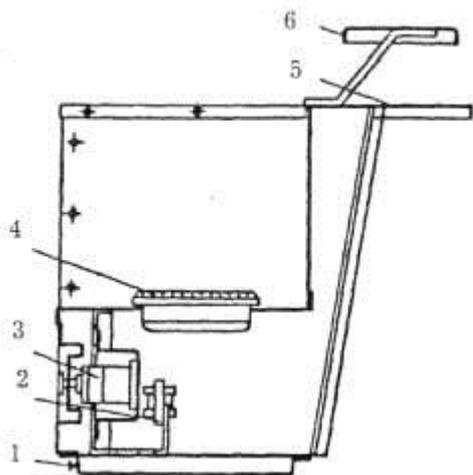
Мармит для первых блюд ЭПМ-5: 1 — болт для присоединения к сети защитного заземления; 2 — щиток для электроподводки; 3 — пакетный переключатель; 4 — конфорка; 5 — стол; 6 — полка
